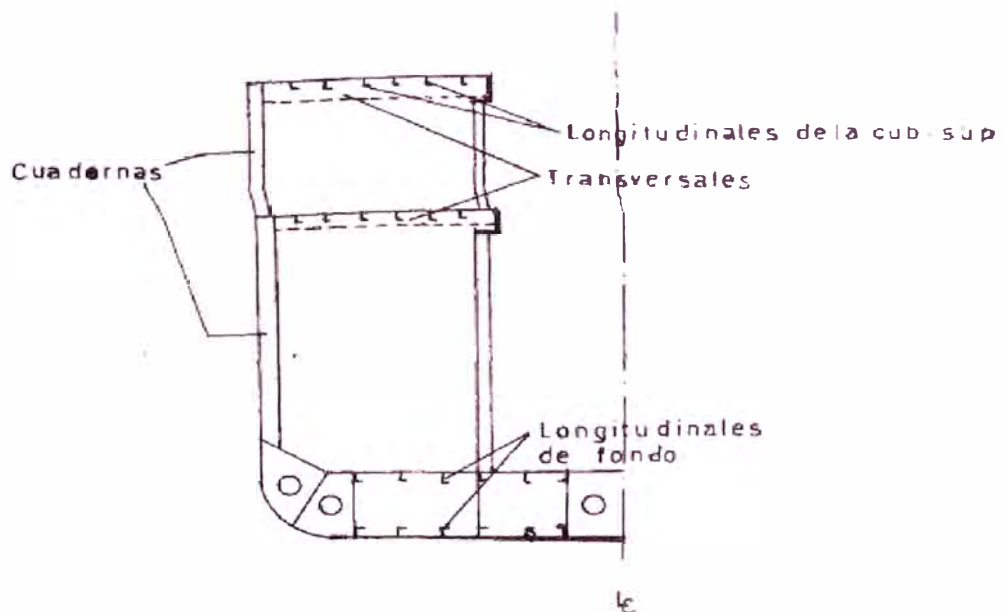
Sección transversal de un buque con cubierta y fondo reforzados longitudinalmente.
